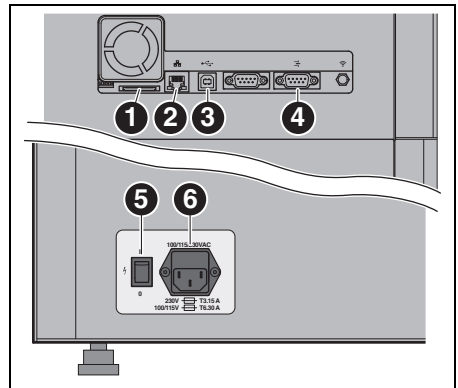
Interfaces sur la face arrière de la fraiseuse
